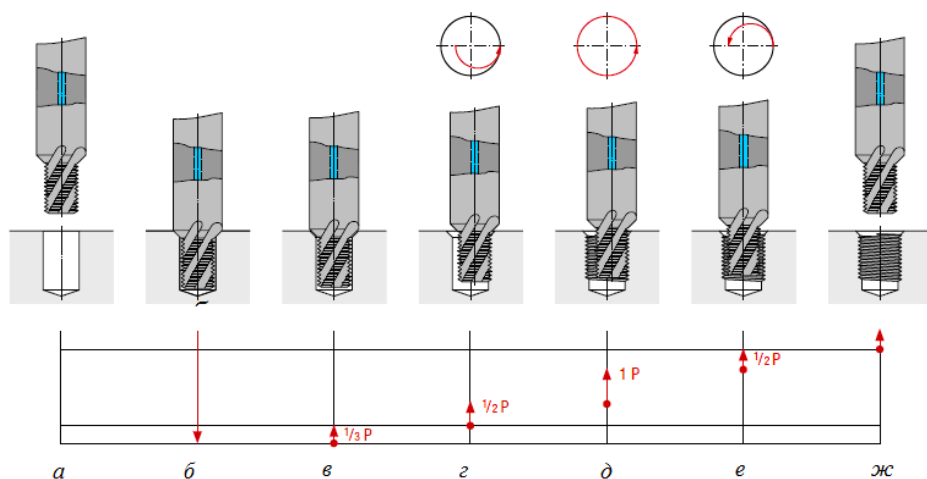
Кинематическая схема процесса обработки резьбовой фрезой с фаскообразующей ступенью [7]
